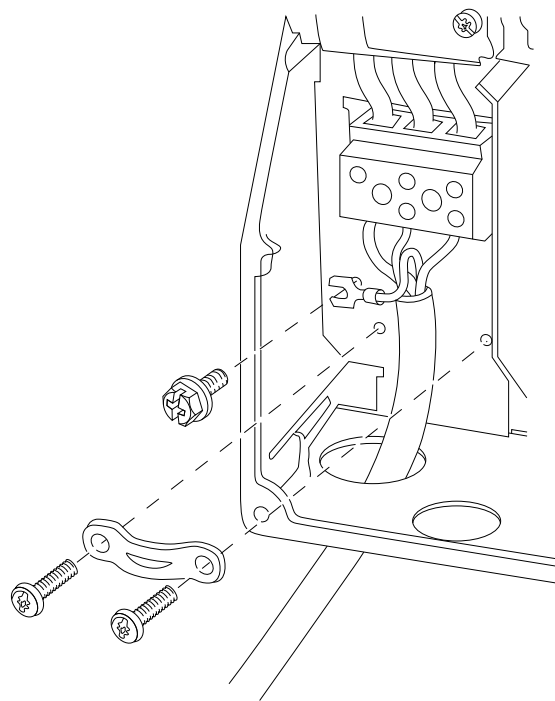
IP54, размеры корпуса I2, I3, I4
